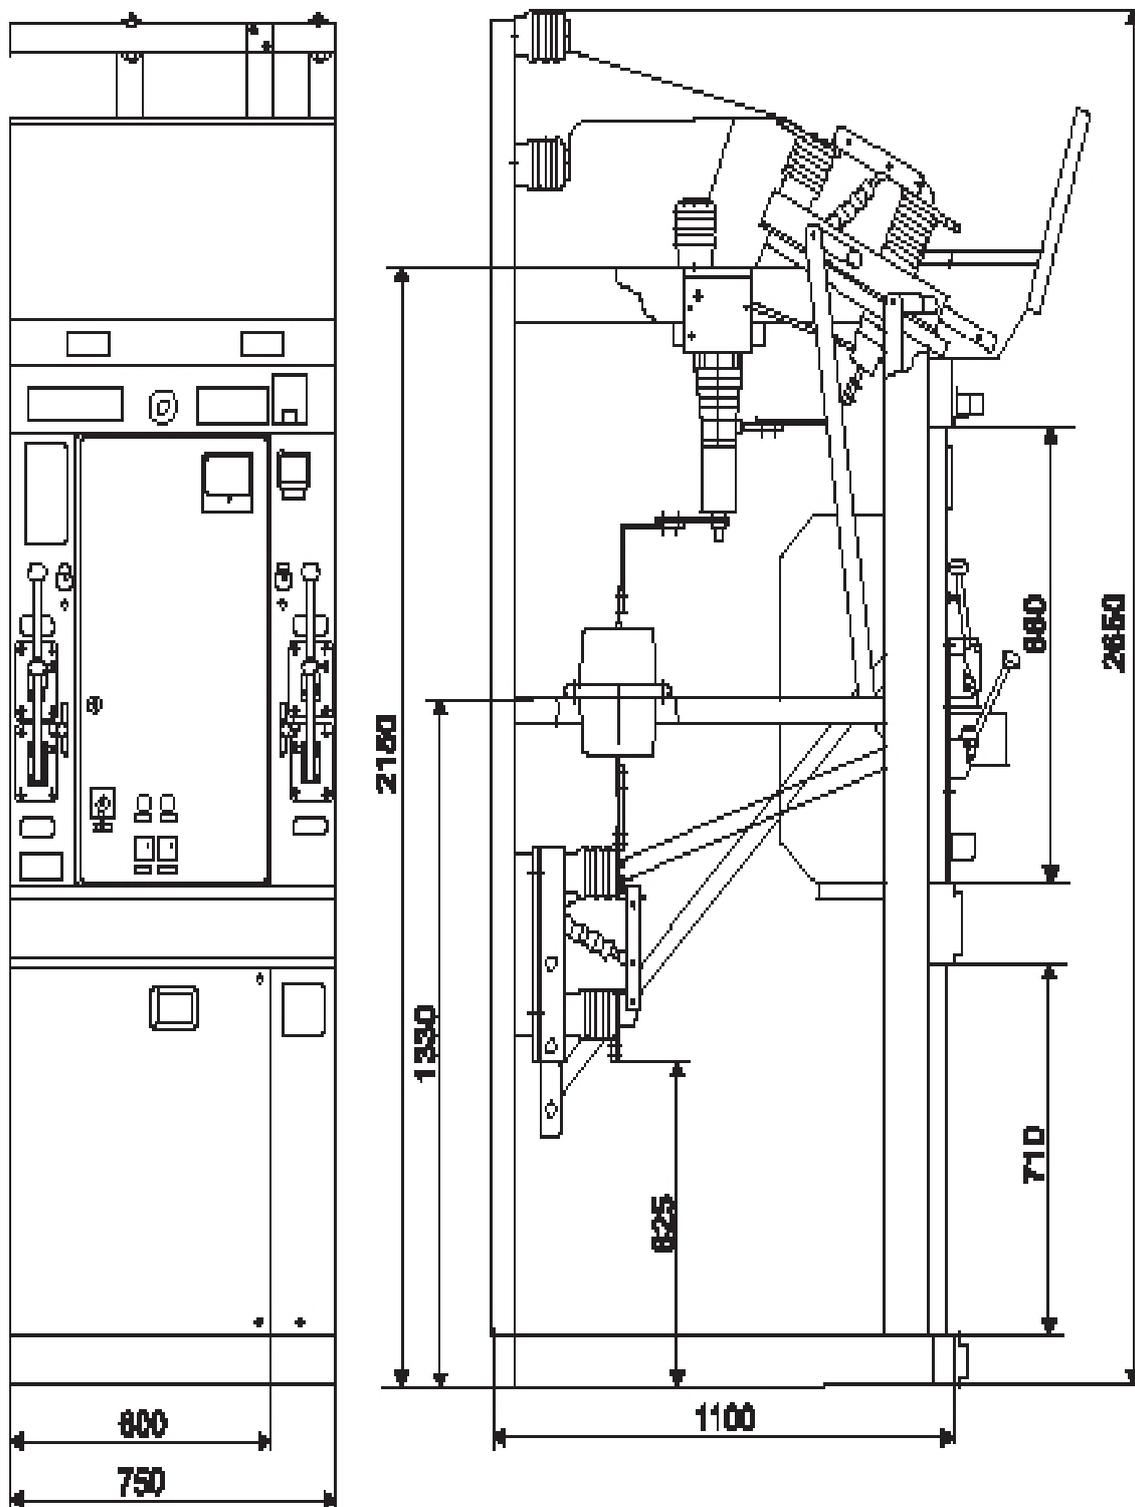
Внешний вид и габаритные размеры камер КСО-298
